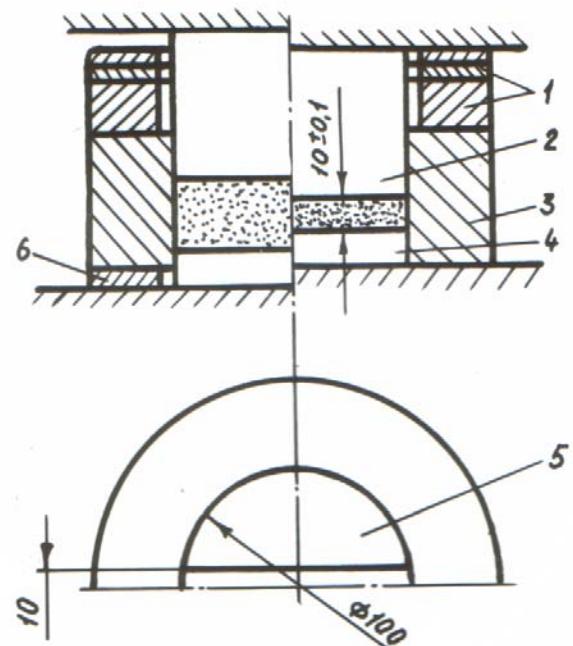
Пресс-форма для холодного прессования образцов на изгиб
